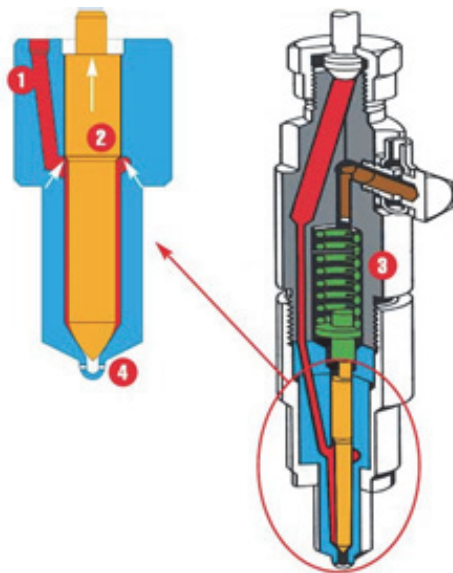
Устройство механической форсунки [3]: 1 – канал подачи топлива; 2 – запорная игла; 3 – пружина; 4 – отверстия распылителя
